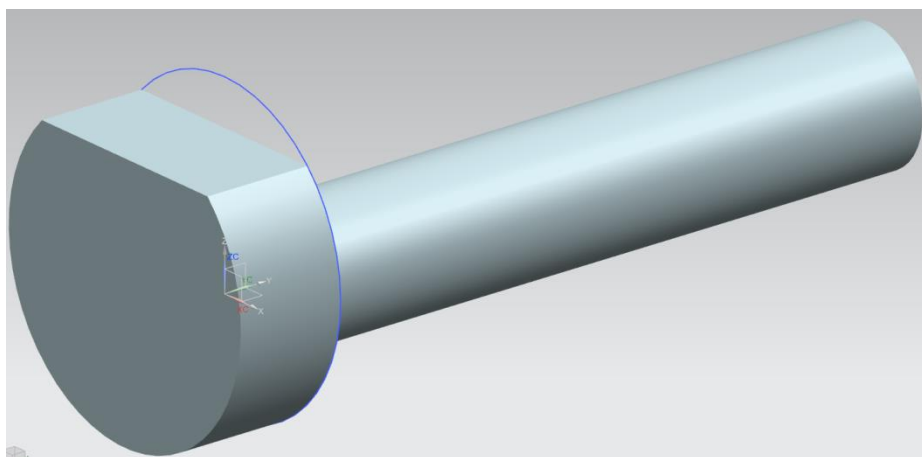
Внешний вид детали после обрезки корпуса улитки
